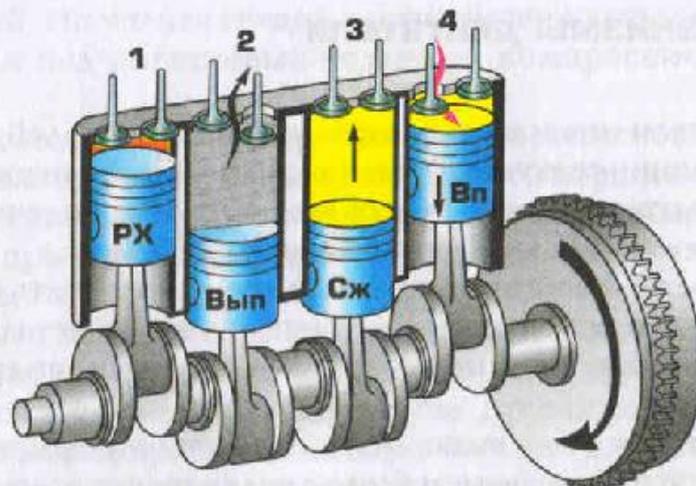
Схема работы четырехцилиндрового двигателя:
